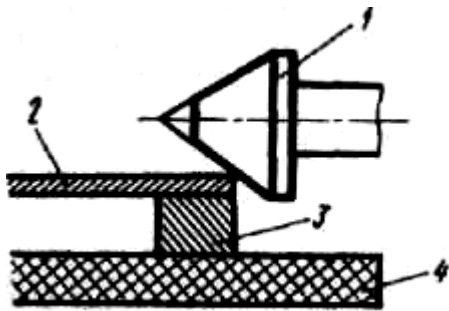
Электрод для роликовой сварки при герметизации корпусов микросхем:
